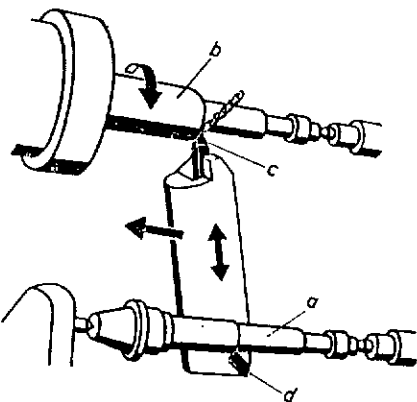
2. Torneo según plantilla. a) Pieza que sirve de muestra; b) pieza que se mecaniza; c) útil de tornearse; d) punzón.
